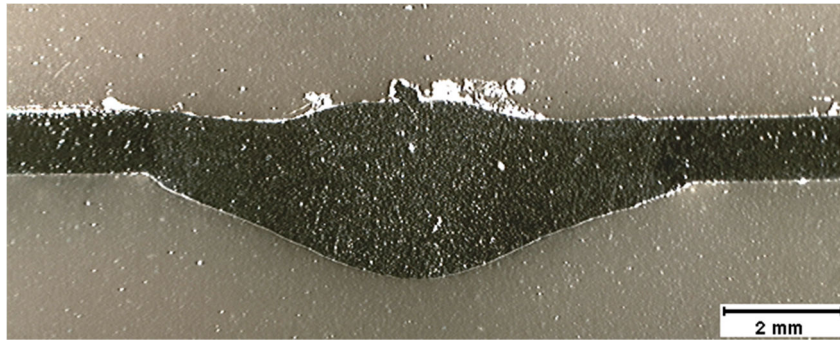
Macrografia (10x) de cordão de solda da classe cratera. Seção transversal L-L do cordão de solda nº 27 – Figura 5.6. Fonte: Autor.
